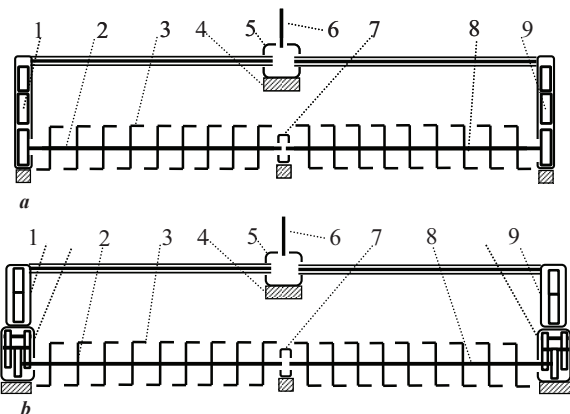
Культиватор фрезерного типа КФГ-3,6 (а) и модель культиватора с мальтийским механизмом в приводе (б):
